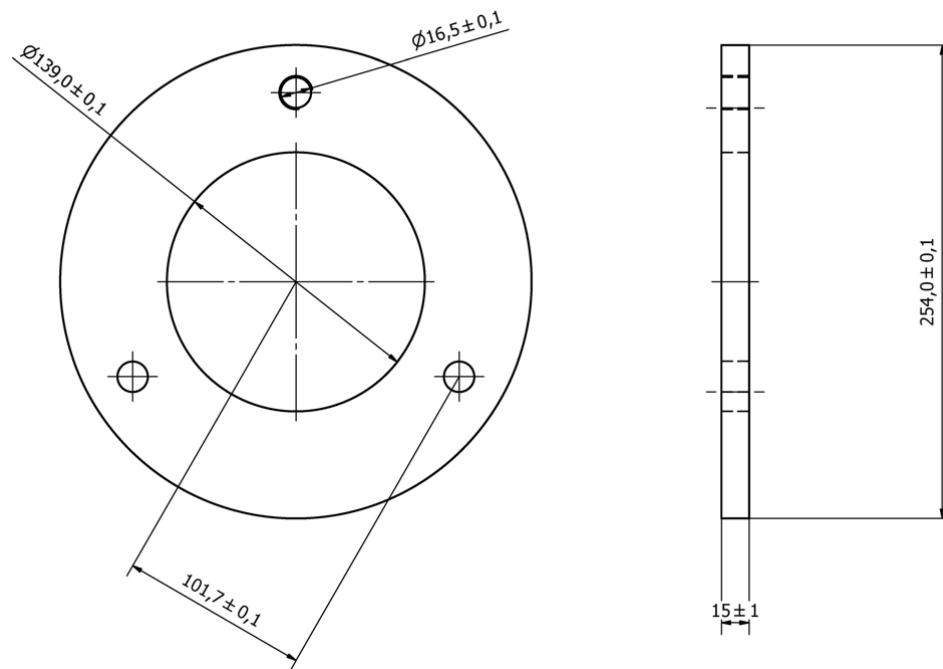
Dimensiones nuevo acoplado rotatorio.
